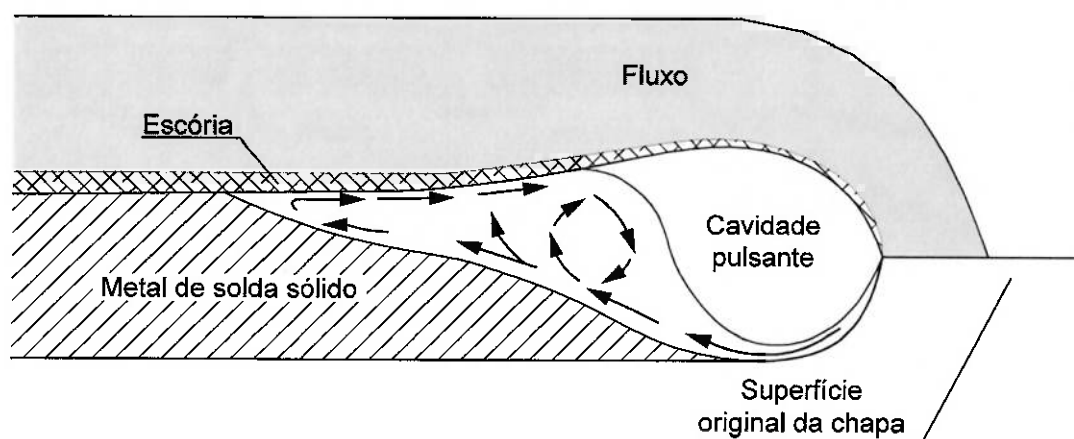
Movimento típico do metal fundido no interior da poça de fusão na soldagem por arco submerso [12].
